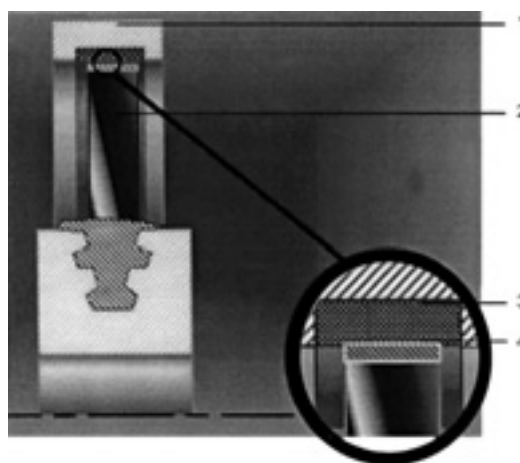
Принципиальная схема регулировки зазоров в ГТД: 1 — деталь корпуса; 2 — перо лопатки; 3 — истираемое уплотнение; 4 — упрочненный торец пера
